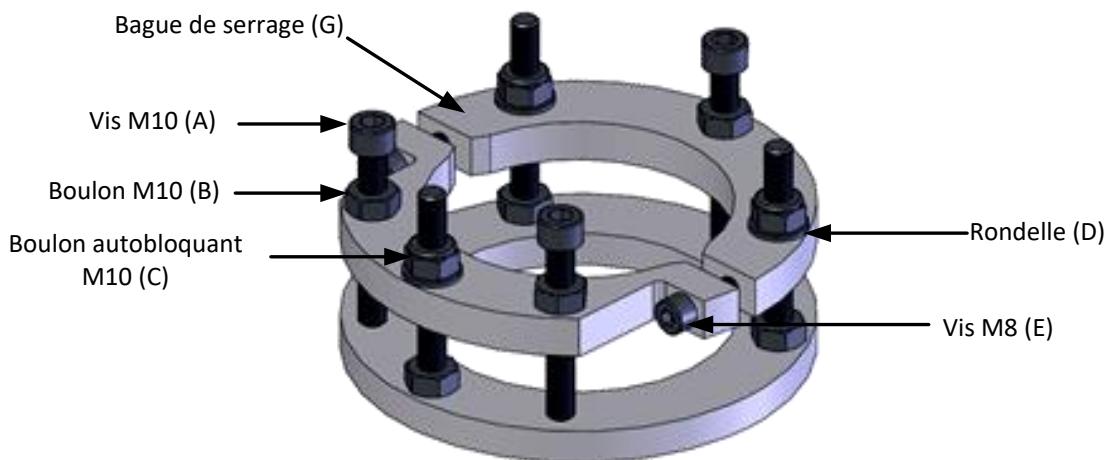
bague de serrage universelle assemblée et installée sur la plaque de fixation
